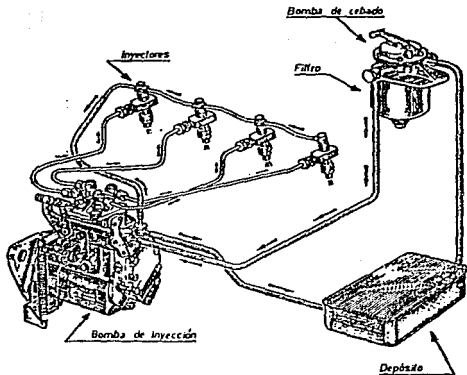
Sistema de inyección de elemento de bombeo único y distribuidor (Silto) en un motor de 4 cilindros.
